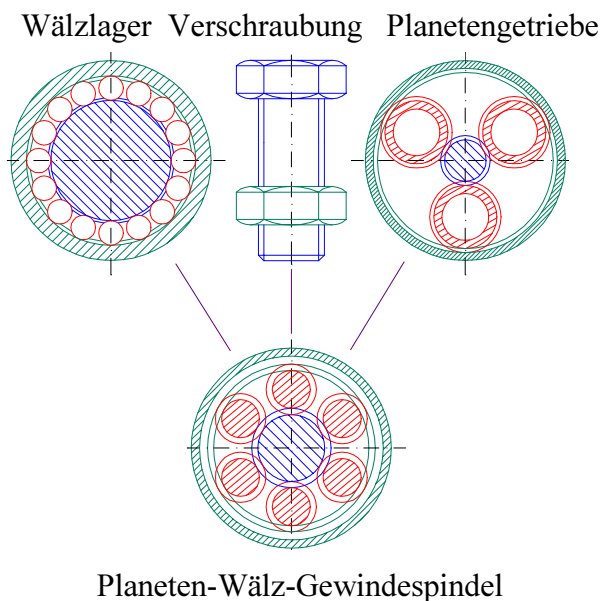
Verwandtschaft zu anderen Maschinenelementen
